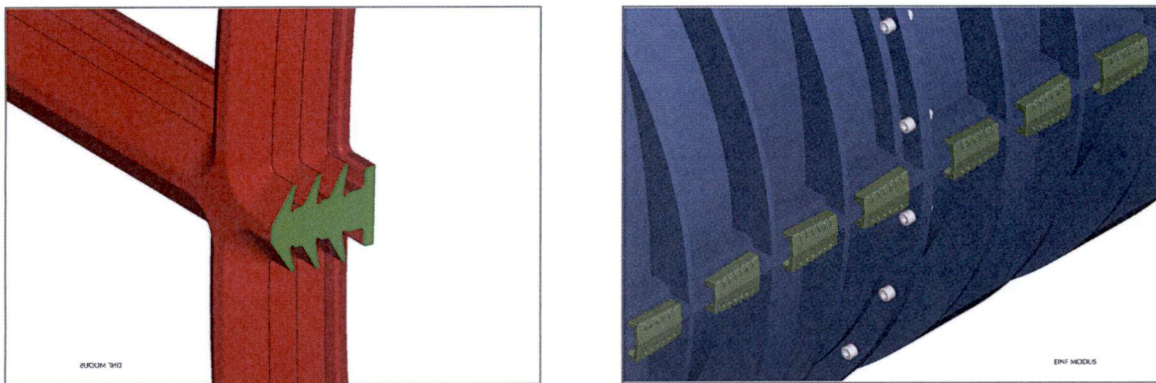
Tankviertel // Ausschnitt Dichtungsprofil Schnittfläche (links), zusammengesetztes Tanksegment mit Schrauben und Klammern (rechts)
